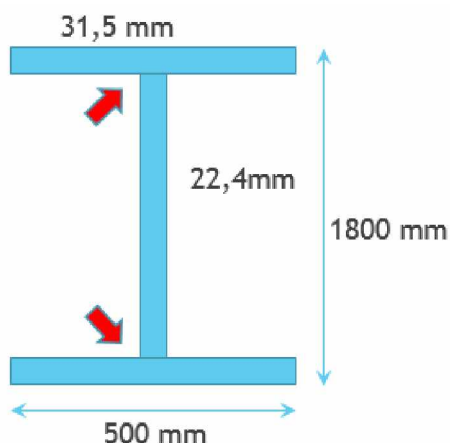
Perfil soldado mais crítico em processo SAW
